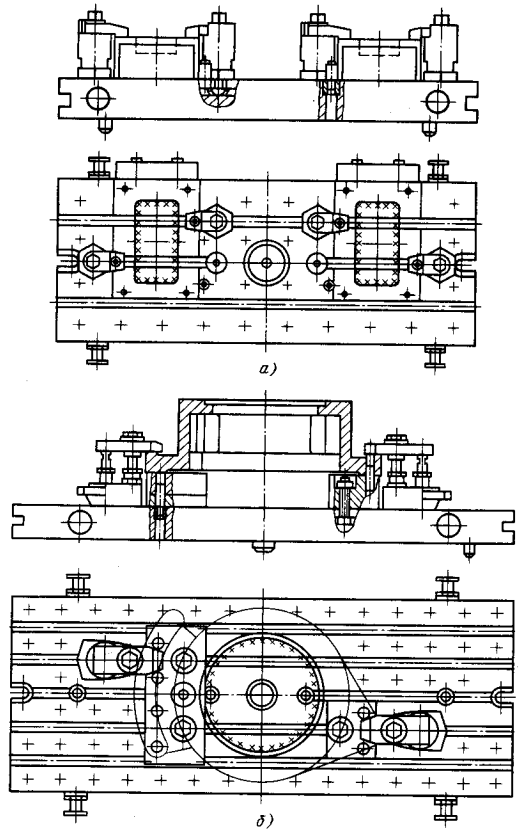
СРП для оснащения станков с ЧПУ: а – фрезерных; б – расточных
